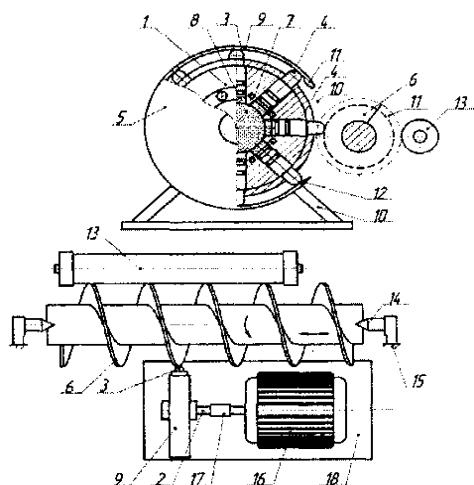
Конструктивна схема інструменту для зміцнення гвинтових поверхонь робочих органів
